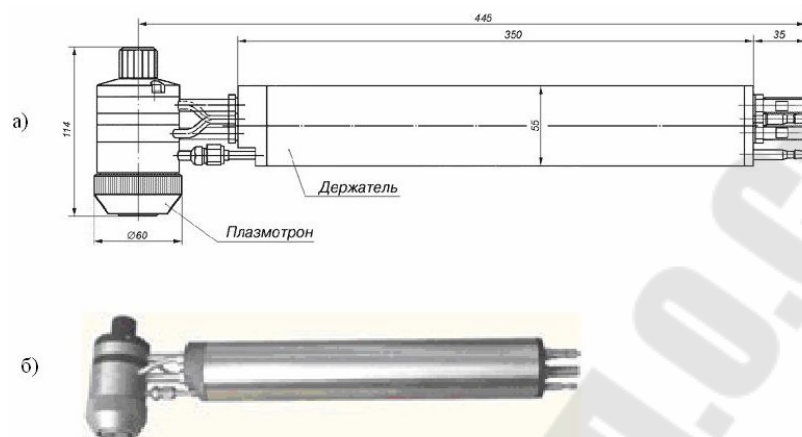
Универсальный плазмотрон для плазменно-порошковой наплавки ПП-6-03: а – схема плазмотрона; б – внешний вид
